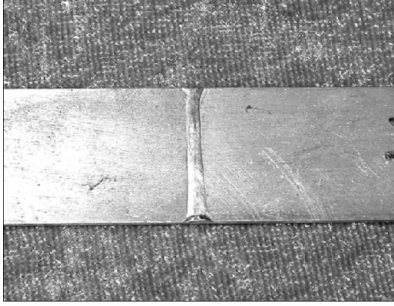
铝合金激光焊缝外观形貌(激光功率 1700 W,扫描速度 600 mm/min,光斑直径 1.2 mm,氩气保护)
